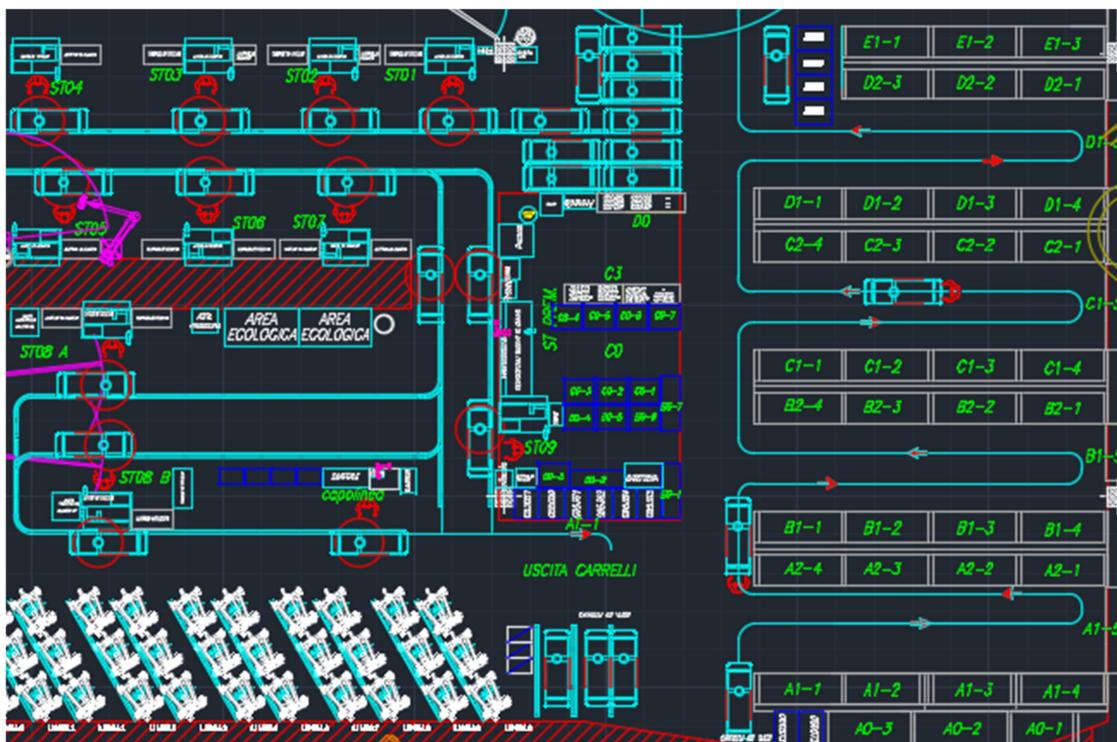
Layout del magazzino motori (MM) e della rispettiva linea di assemblaggio
